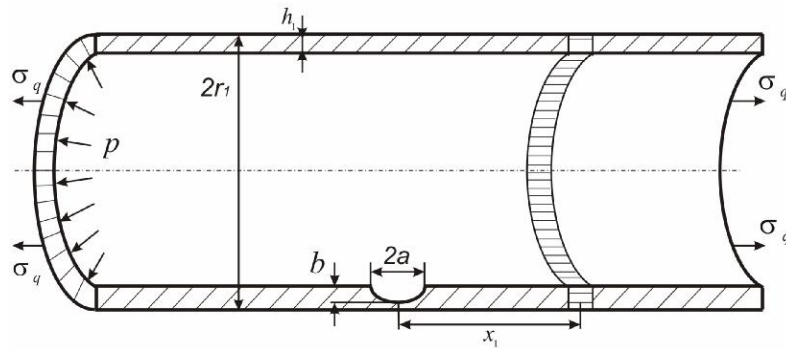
Схема навантаження зварного з'єднання трубопроводу з тріщиною
